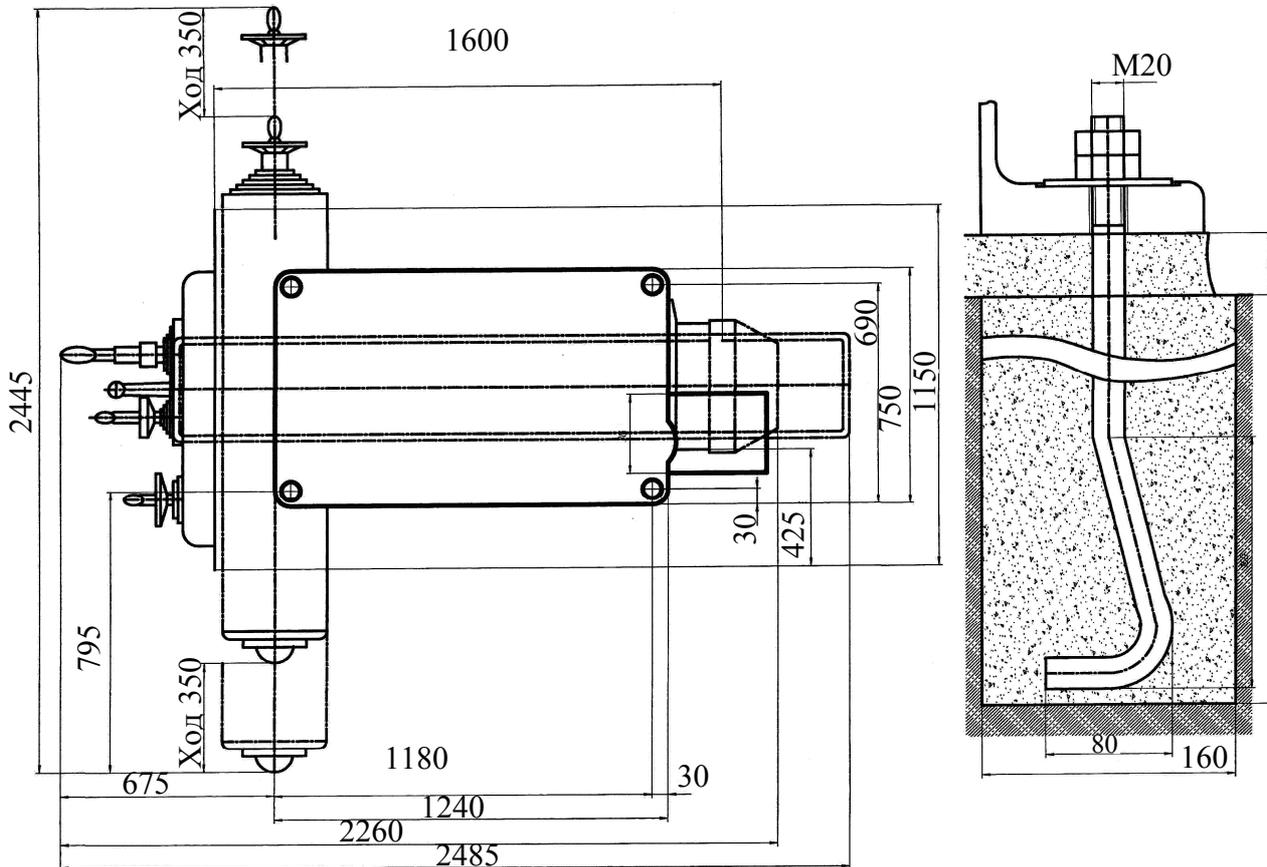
Установочный чертеж горизонтально-фрезерного станка 6М82
